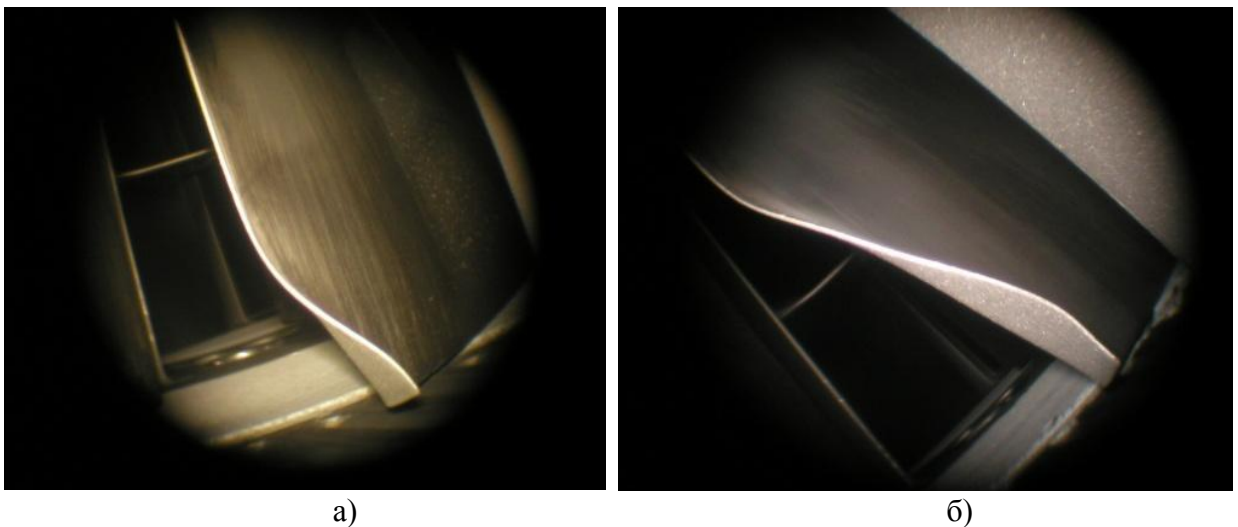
Загибы уголков лопаток компрессора двигателя ПС-90А (а-б) [8]
